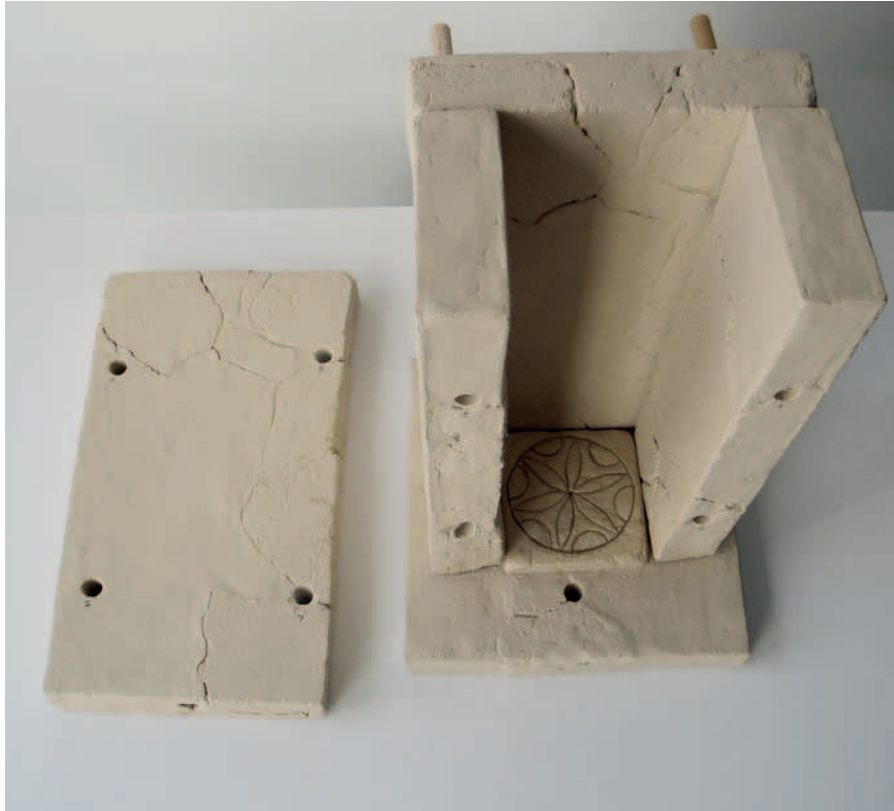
Assemblage des fragments du moule (n° inv. Wi 1855,09; 03; 04; 12).
